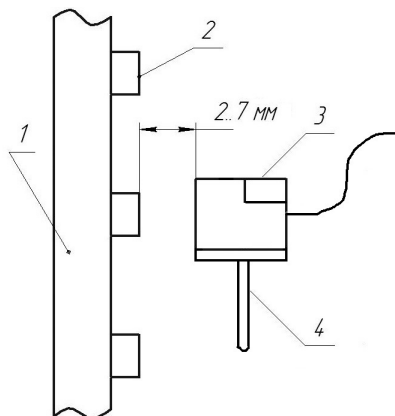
Монтажная схема датчика скорости: 1 – диск колеса; 2 – металлические детали, закрепленные на диске колеса; 3 – датчик; 4 – кронштейн крепления
